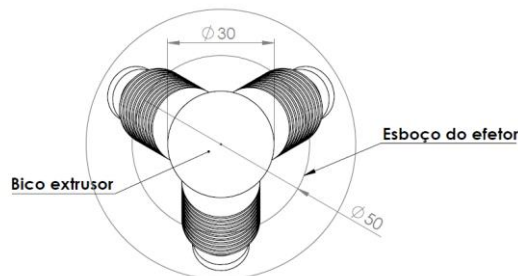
Esboço do efetor para permitir a montagem do *diamond extruder*.
